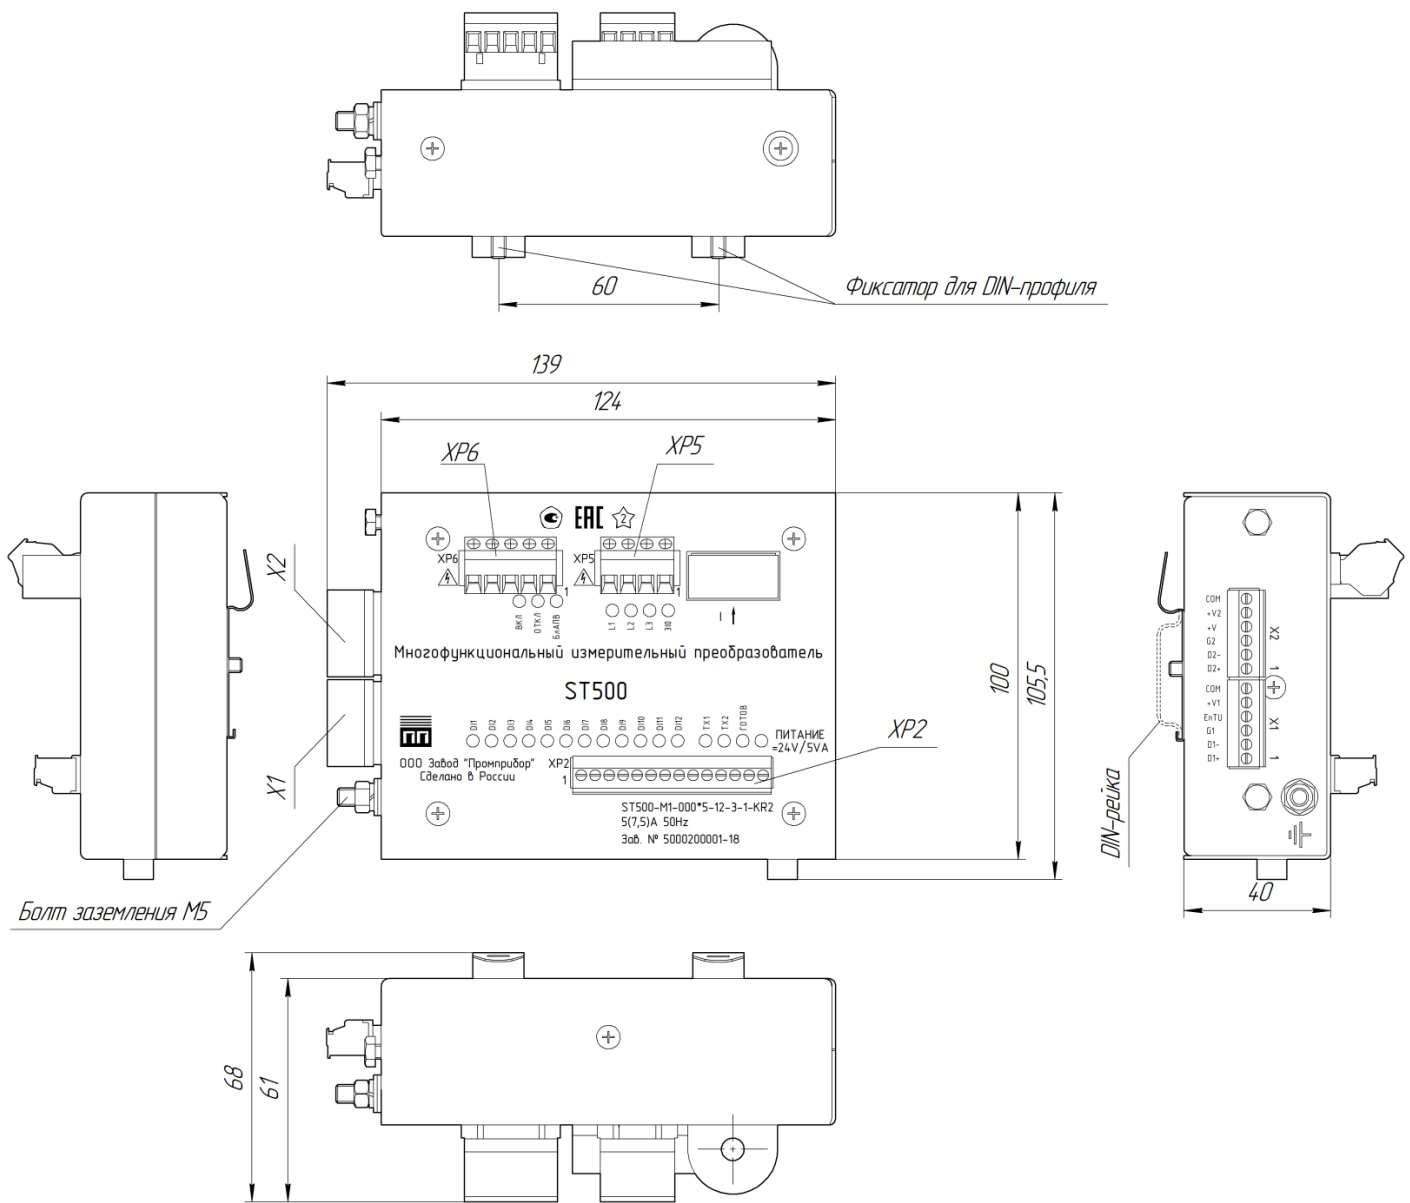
Внешний вид и габаритные размеры МИП
